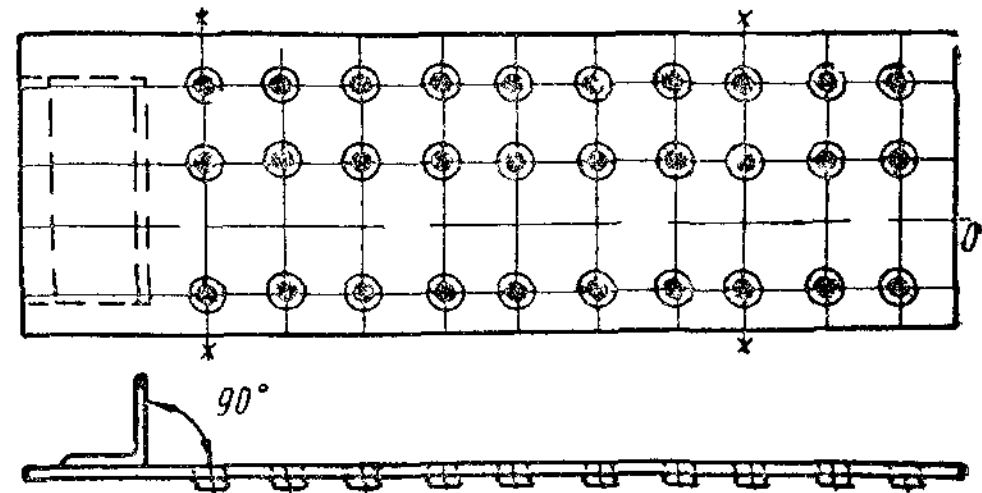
Кондуктор для сверления отверстий в торцовых планках подстропильных ферм
